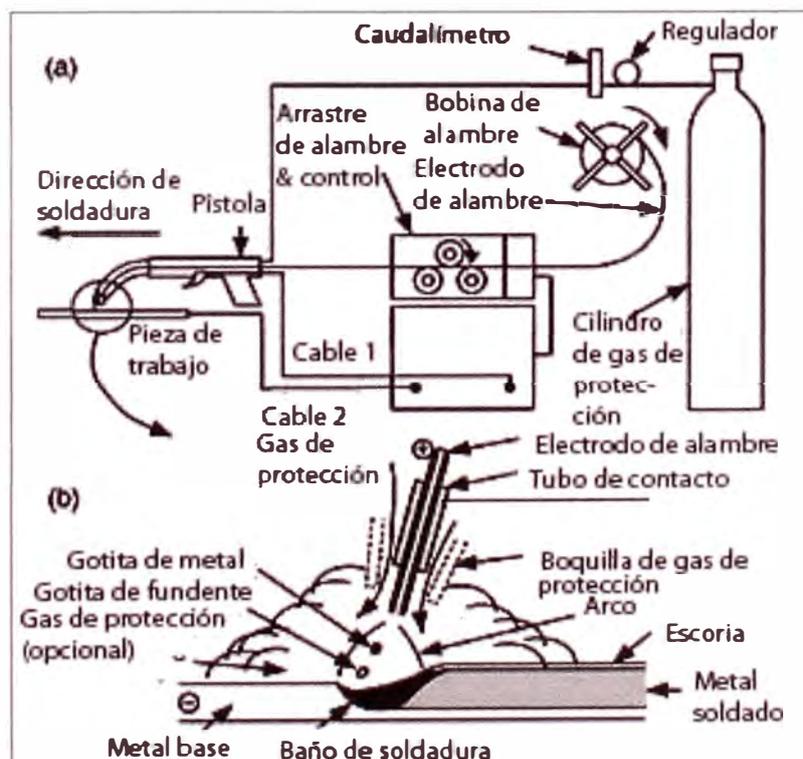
Esquema del proceso de soldadura GMAW
